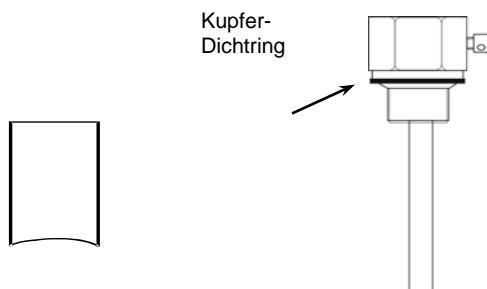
Schweißmuffe Abb. 2: Edelstahl-TauchhülSE
